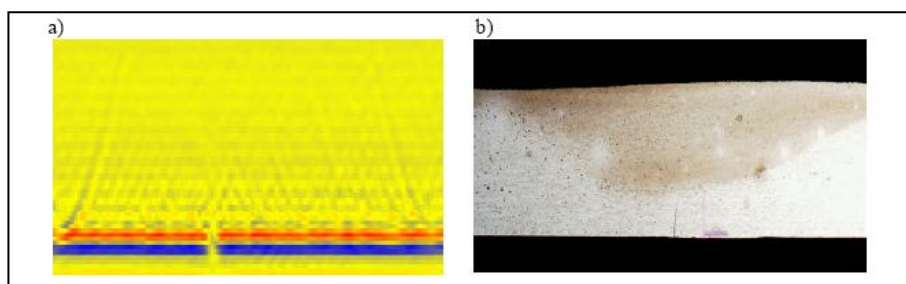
Falta de penetración en soldadura ^[23]
